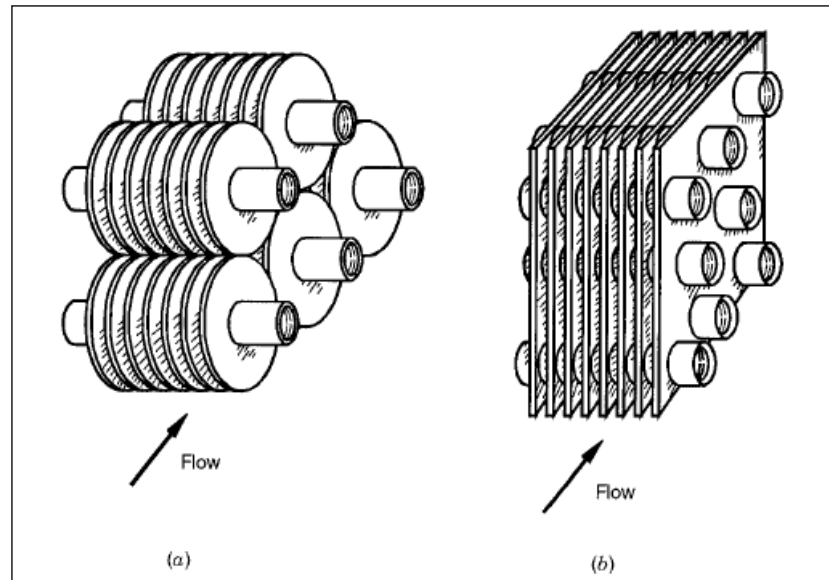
(a) Tubes à ailettes simples; (b) ailettes plaques autour de tubes. Les ailettes sont plates, mais pourraient être ondulées, coupées ou à événements.
